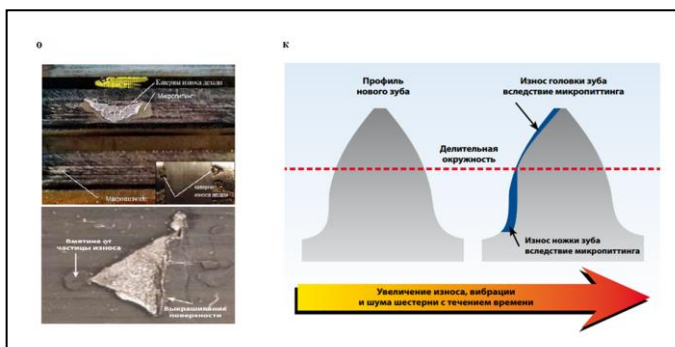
Риски (o) после обработки фрезерования и шлифования зубчатых колес вызывают износ бритвенного инструмента на основании определения структуры шероховатости поверхности микропиттинга на детали (к)
